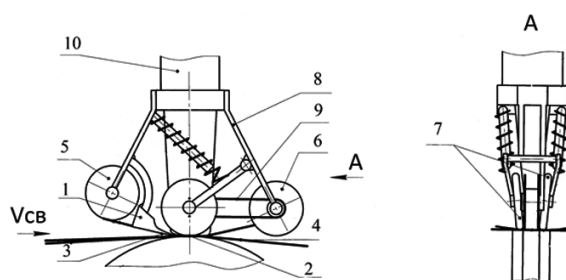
Устройство для непрерывной термоультразвуковой сварки термопластичных пленок
